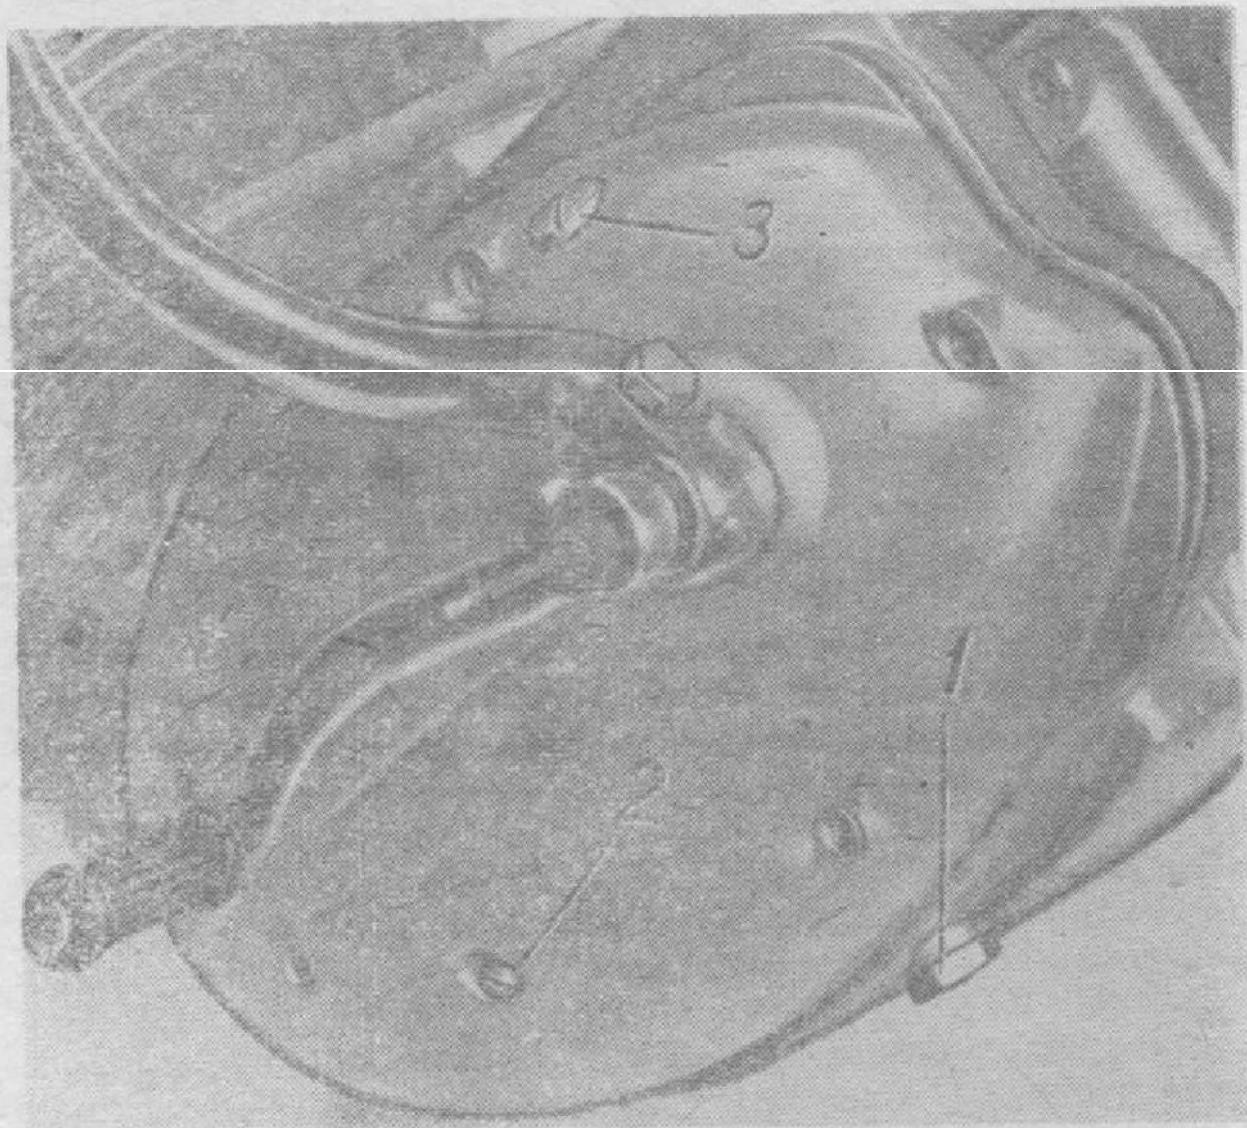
ВИД ДВИГАТЕЛЯ СЛЕВА:
